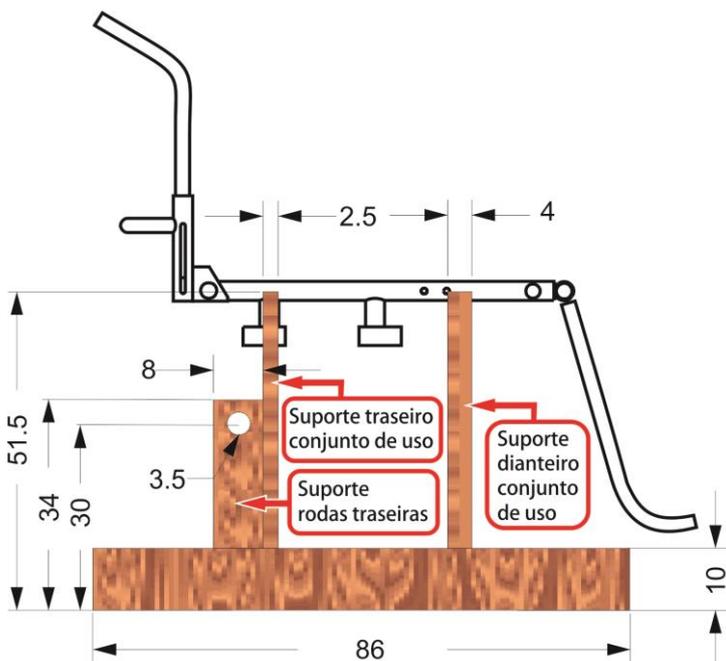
Desenho técnico do gabarito para o suporte do conjunto de uso
